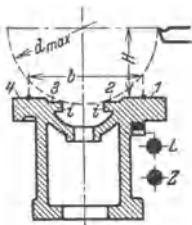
Deutsche Bettform mit rechteckigem Querschnitt.
